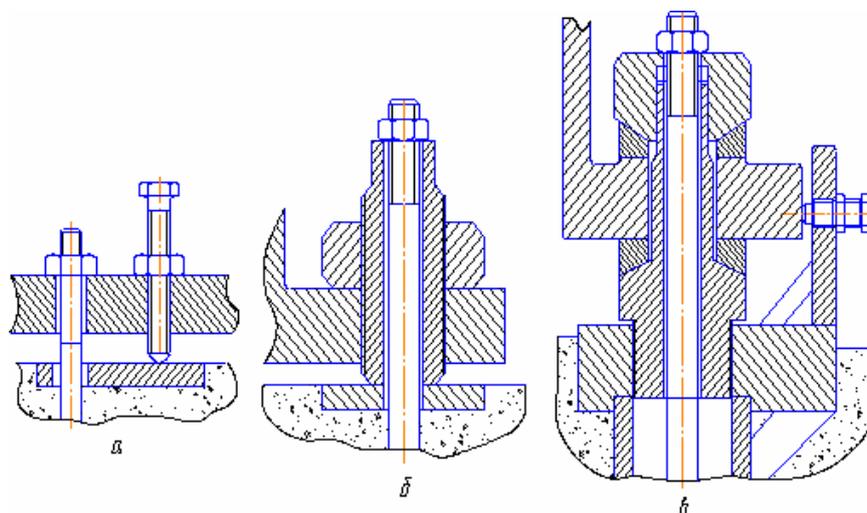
Конструкции винтовых опор, используемых для станков, закрепляемых болтами
